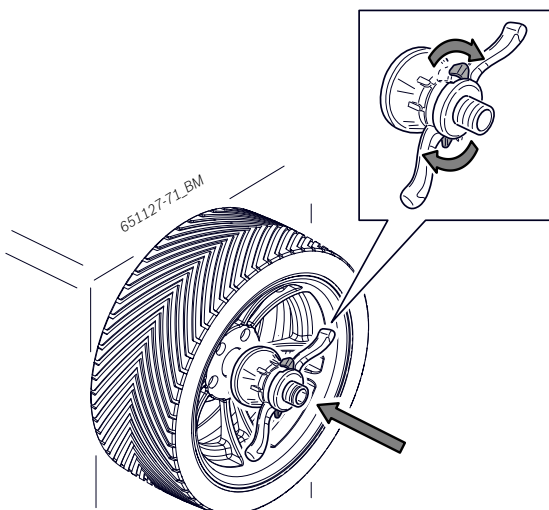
Die Schnellspannmutter entriegelt auf der Welle positionieren
